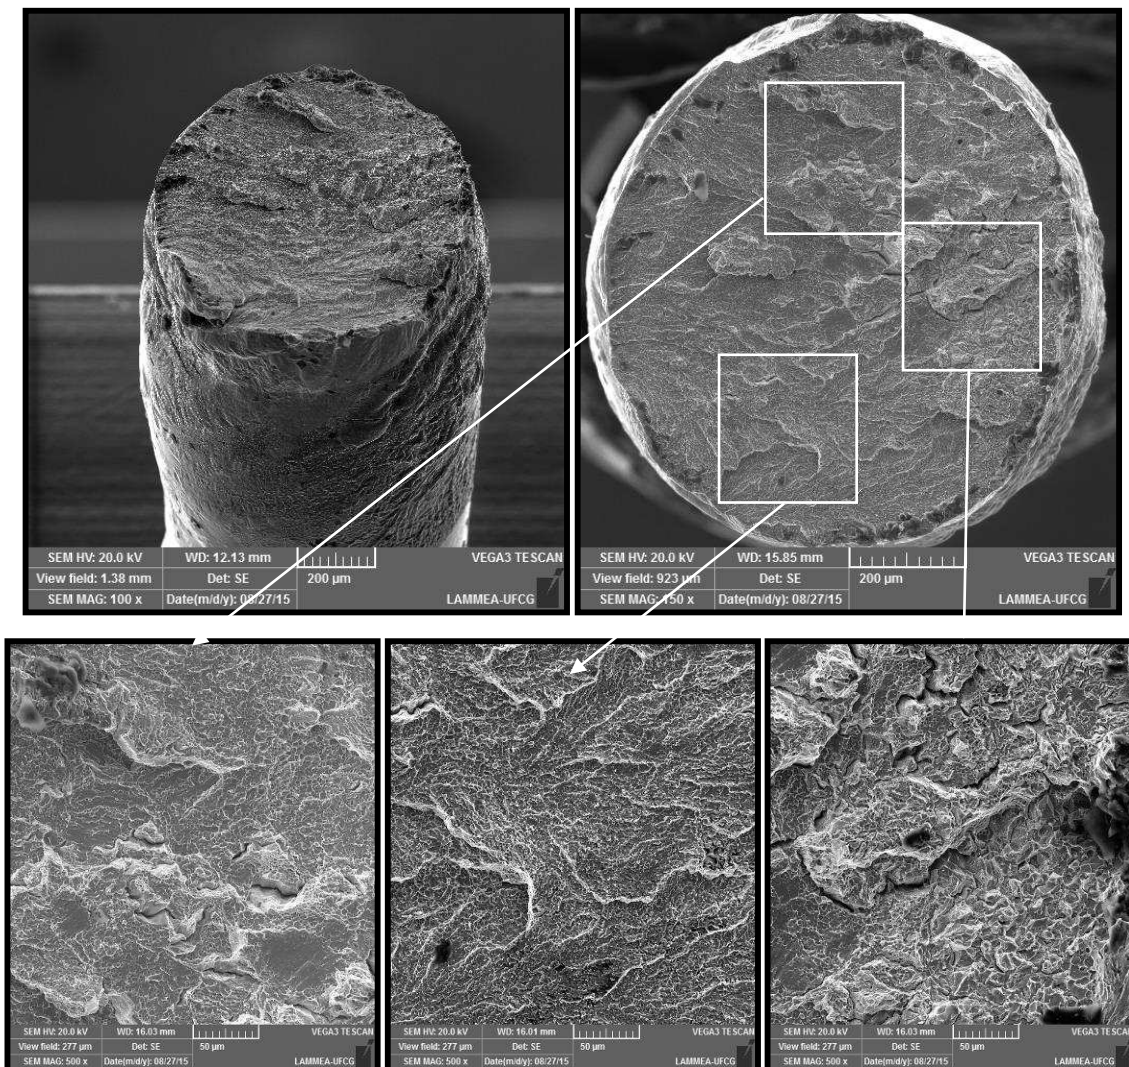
Superfície de fratura do fio atuador soldado na configuração 8ms/65% e testado a 90°C.
